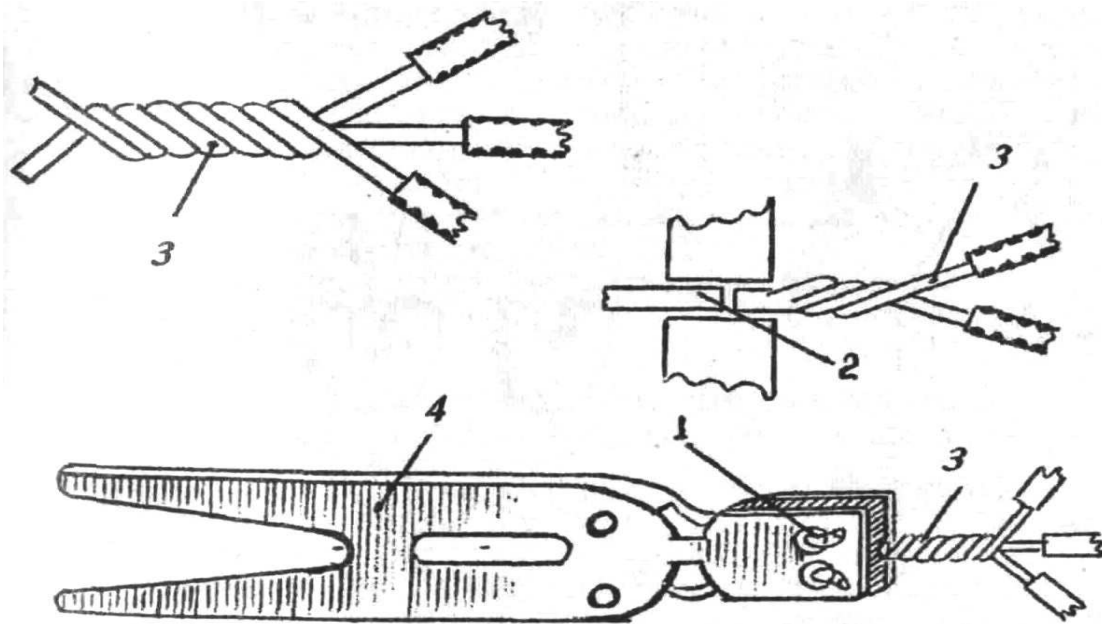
Клеши КСП (процесс опрессовки)
